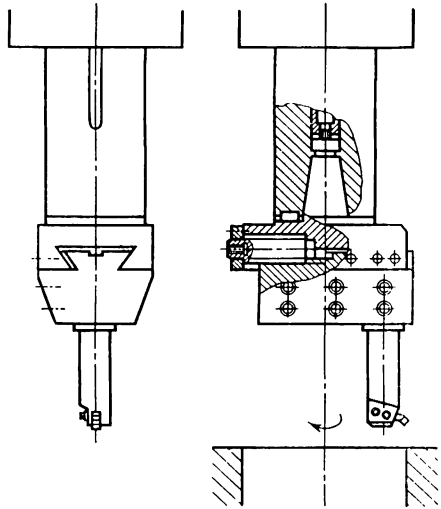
Расточный суппорт с перемещающейся ползушкой для крепления расточной оправки
